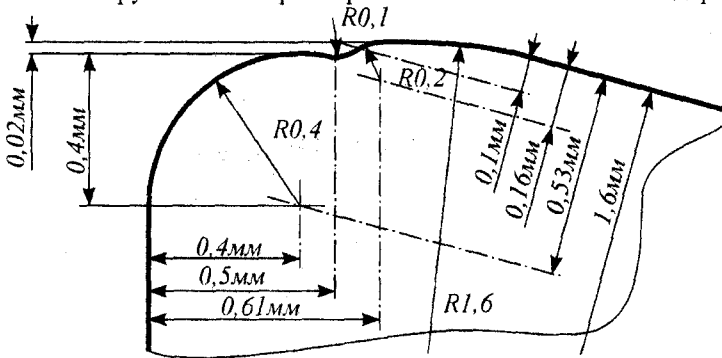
Параметры режущей кромки СМП для чистовой и финишной обработки
